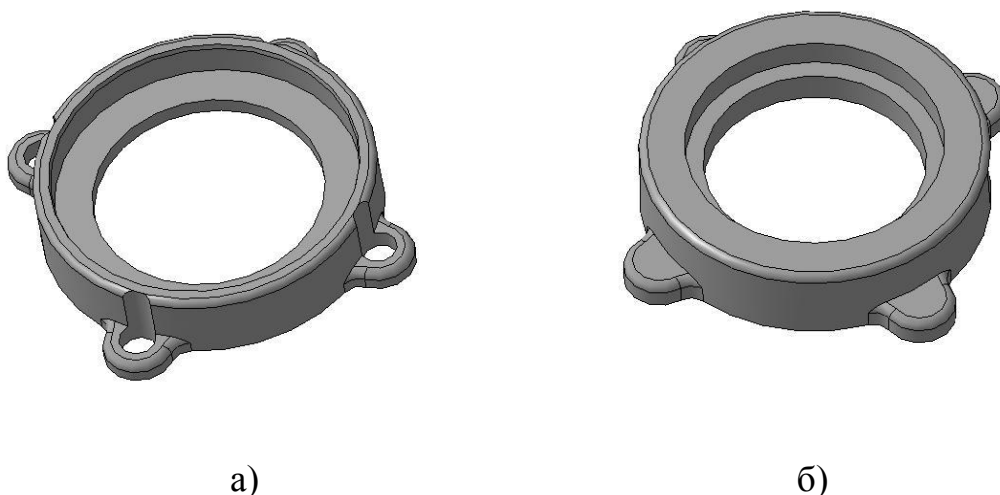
Тривимірні моделі: а- деталі, б- заготовки.
